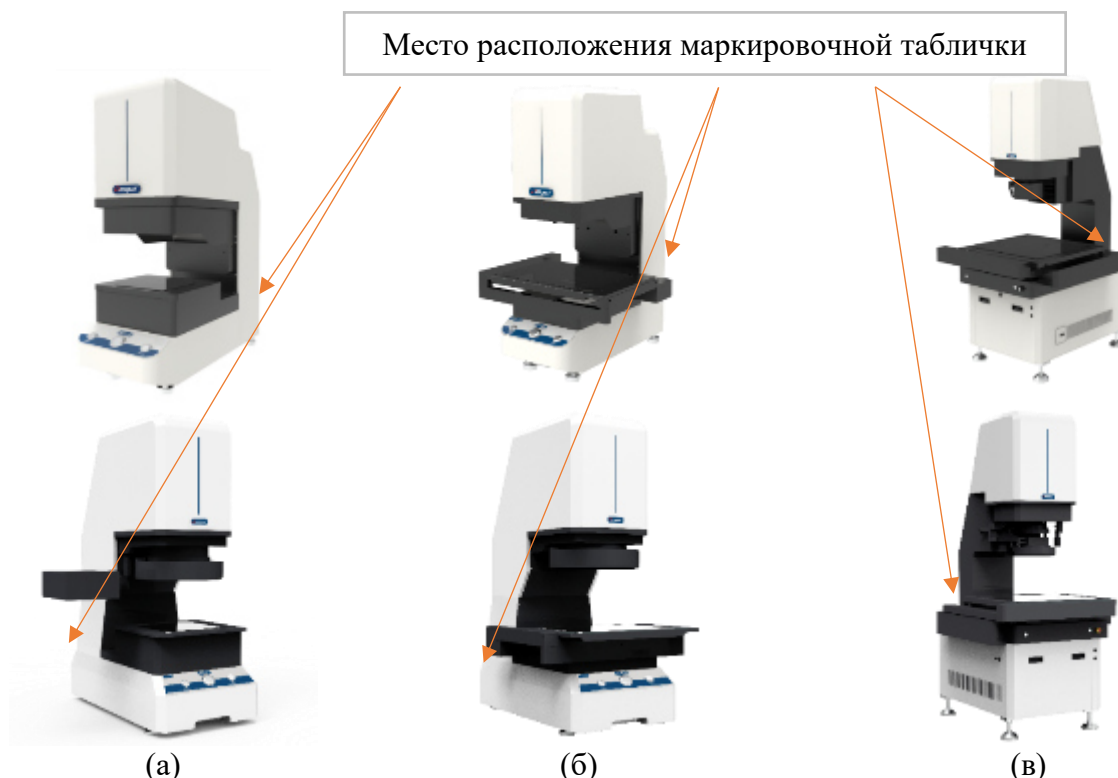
Общий вид ВИМ FlashTester и места расположения маркировочной таблички
